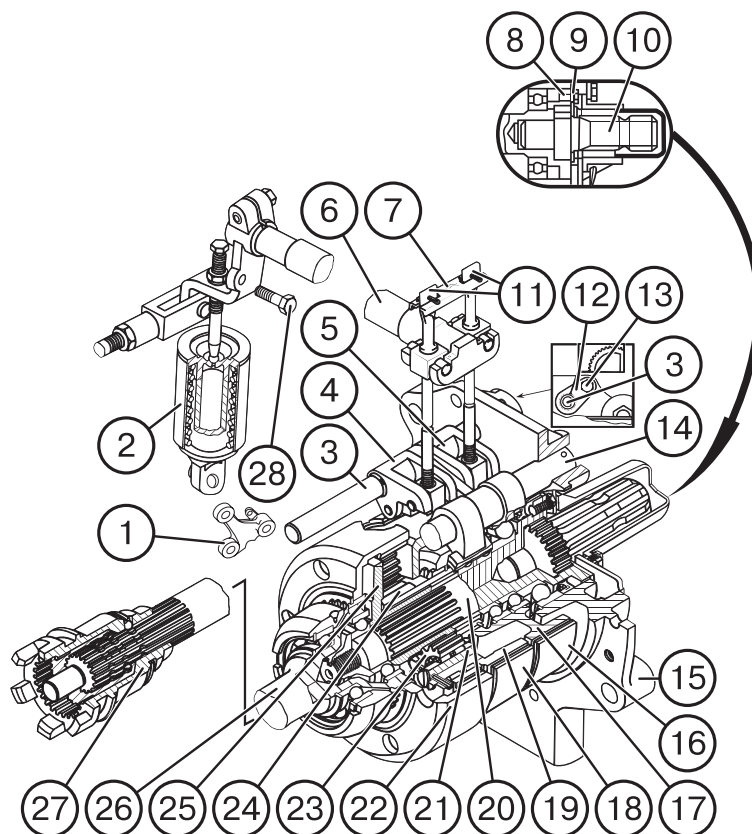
Планетарный редуктор заднего ВОМ:
